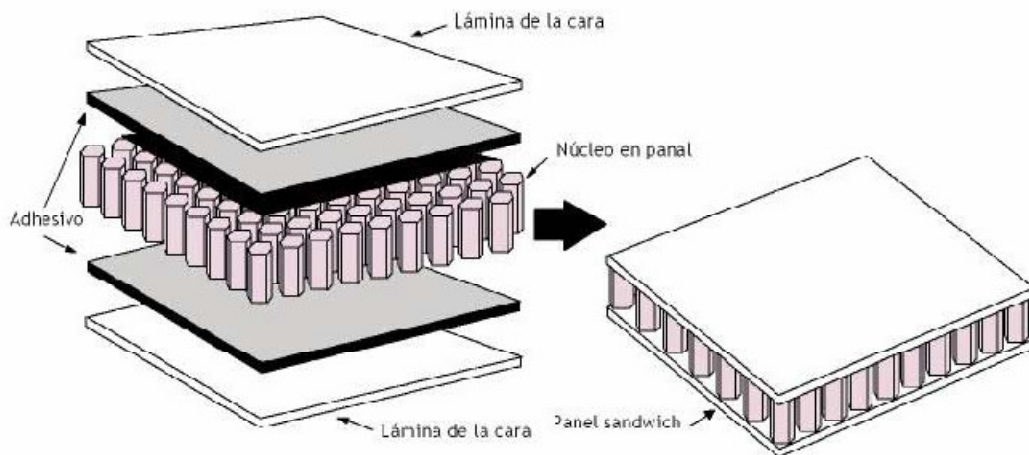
Diagrama esquemático de la fabricación de un panel sándwich con un núcleo en panel
